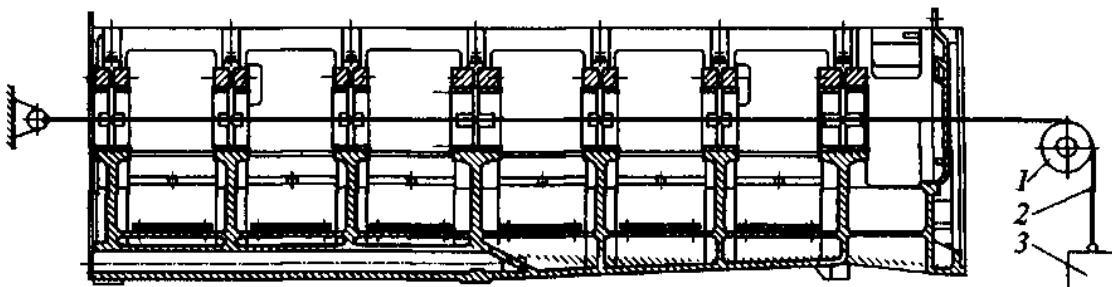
Схема проверки соосности коренных подшипников коленчатого вала дизеля с помощью струнки:
